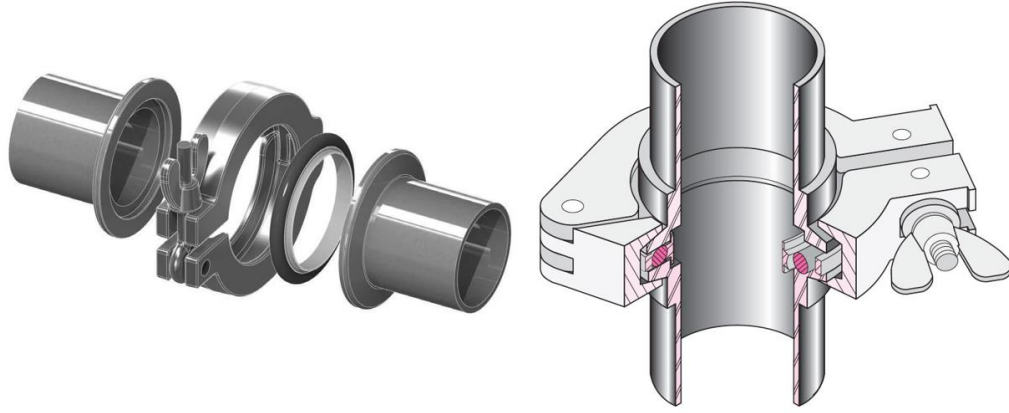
Bakır kutuplar ve tank tabanı arasına o-ring uygulaması
